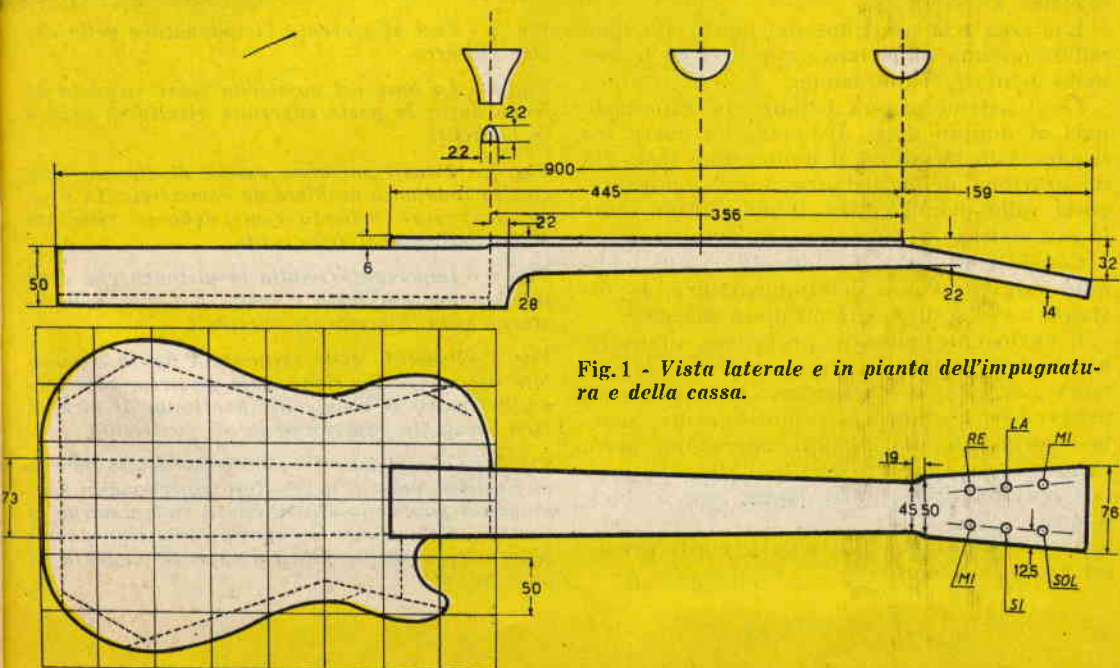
Vista laterale e in pianta dell'impugnatura e della cassa.
